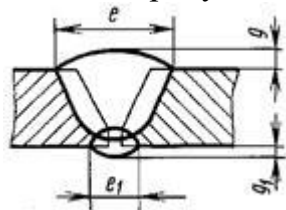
Конструктивные элементы шва сварного соединения, где
